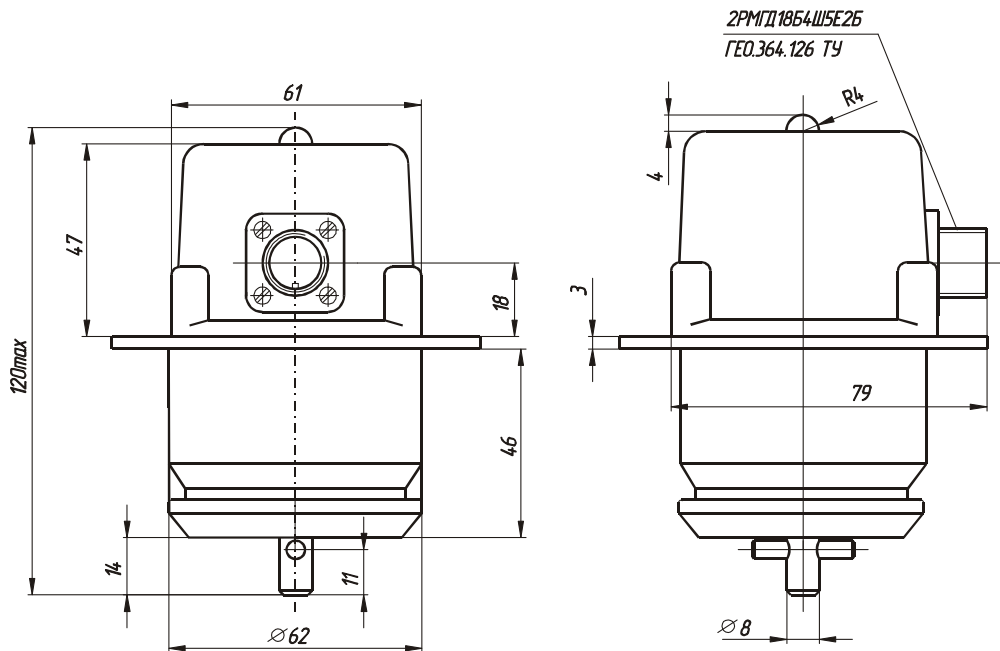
Габаритные и присоединительные размеры датчика азимута
